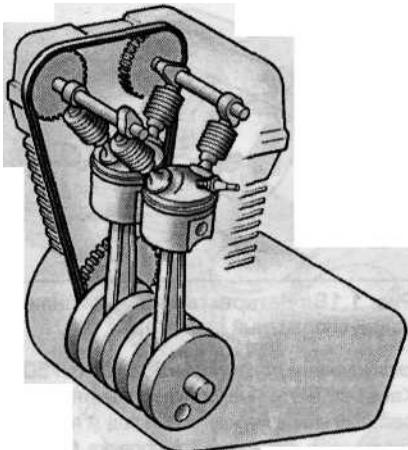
а Четырехтактный рядный двухцилиндровый двигатель с чередованием вспышек через 360 градусов
